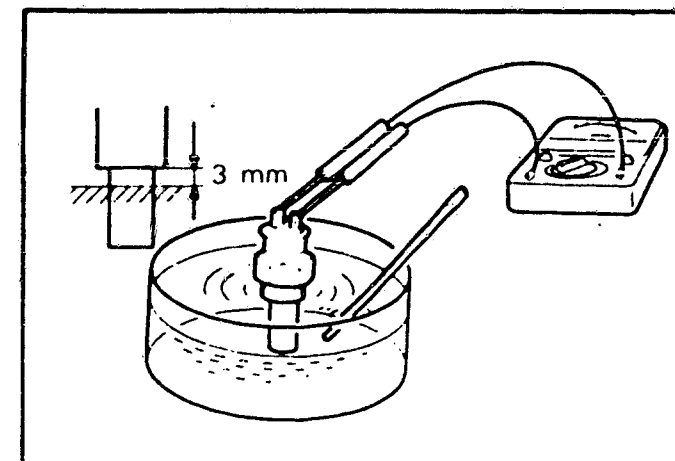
Prüfung des Kühlmitteltemperaturfühlers im Wasserbad.
